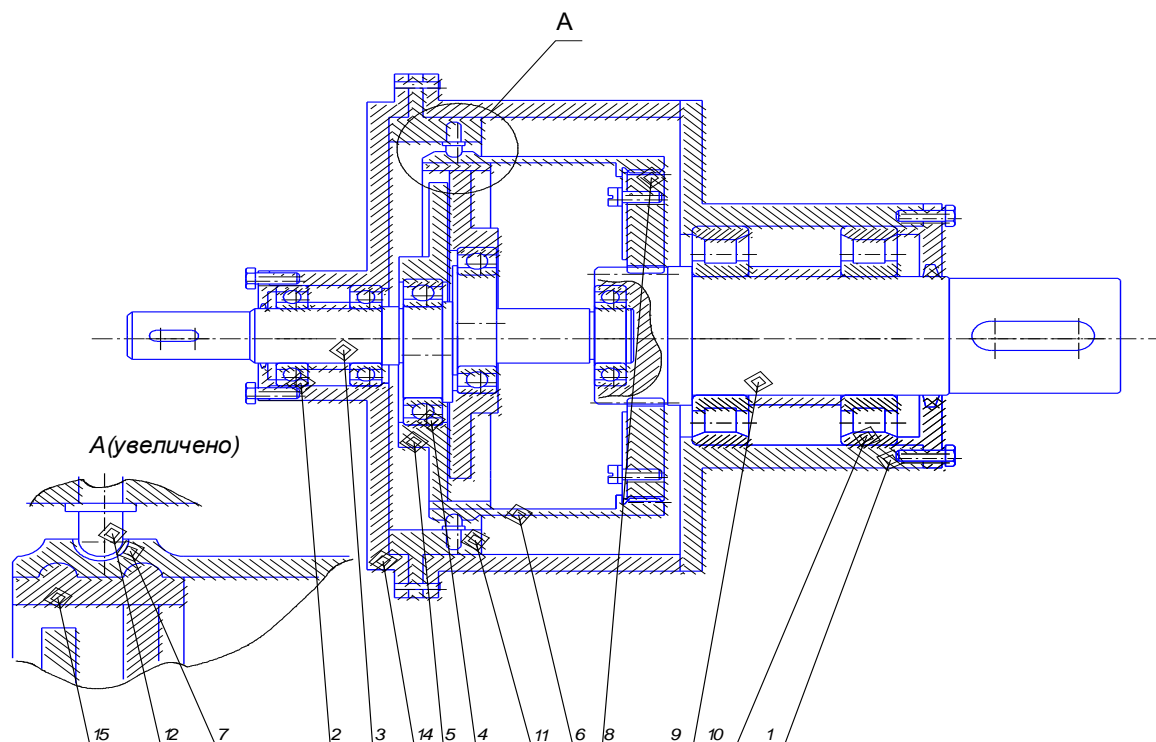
Конструктивная схема ВШП: 1-корпус; 2-подшипники ; 3- эксцентриковый вал ; 4-подшипники ; 5-диски генератора ; 6-гибкое колесо ; 7-сферические углубления ; 8-шлицевое соединение ; 9-выходной вал ; 10-подшипники ; 11-жесткое колесо ; 12-пальцы с шарообразными головками ; 14-крышка редуктора; 15-подкладное кольцо.
